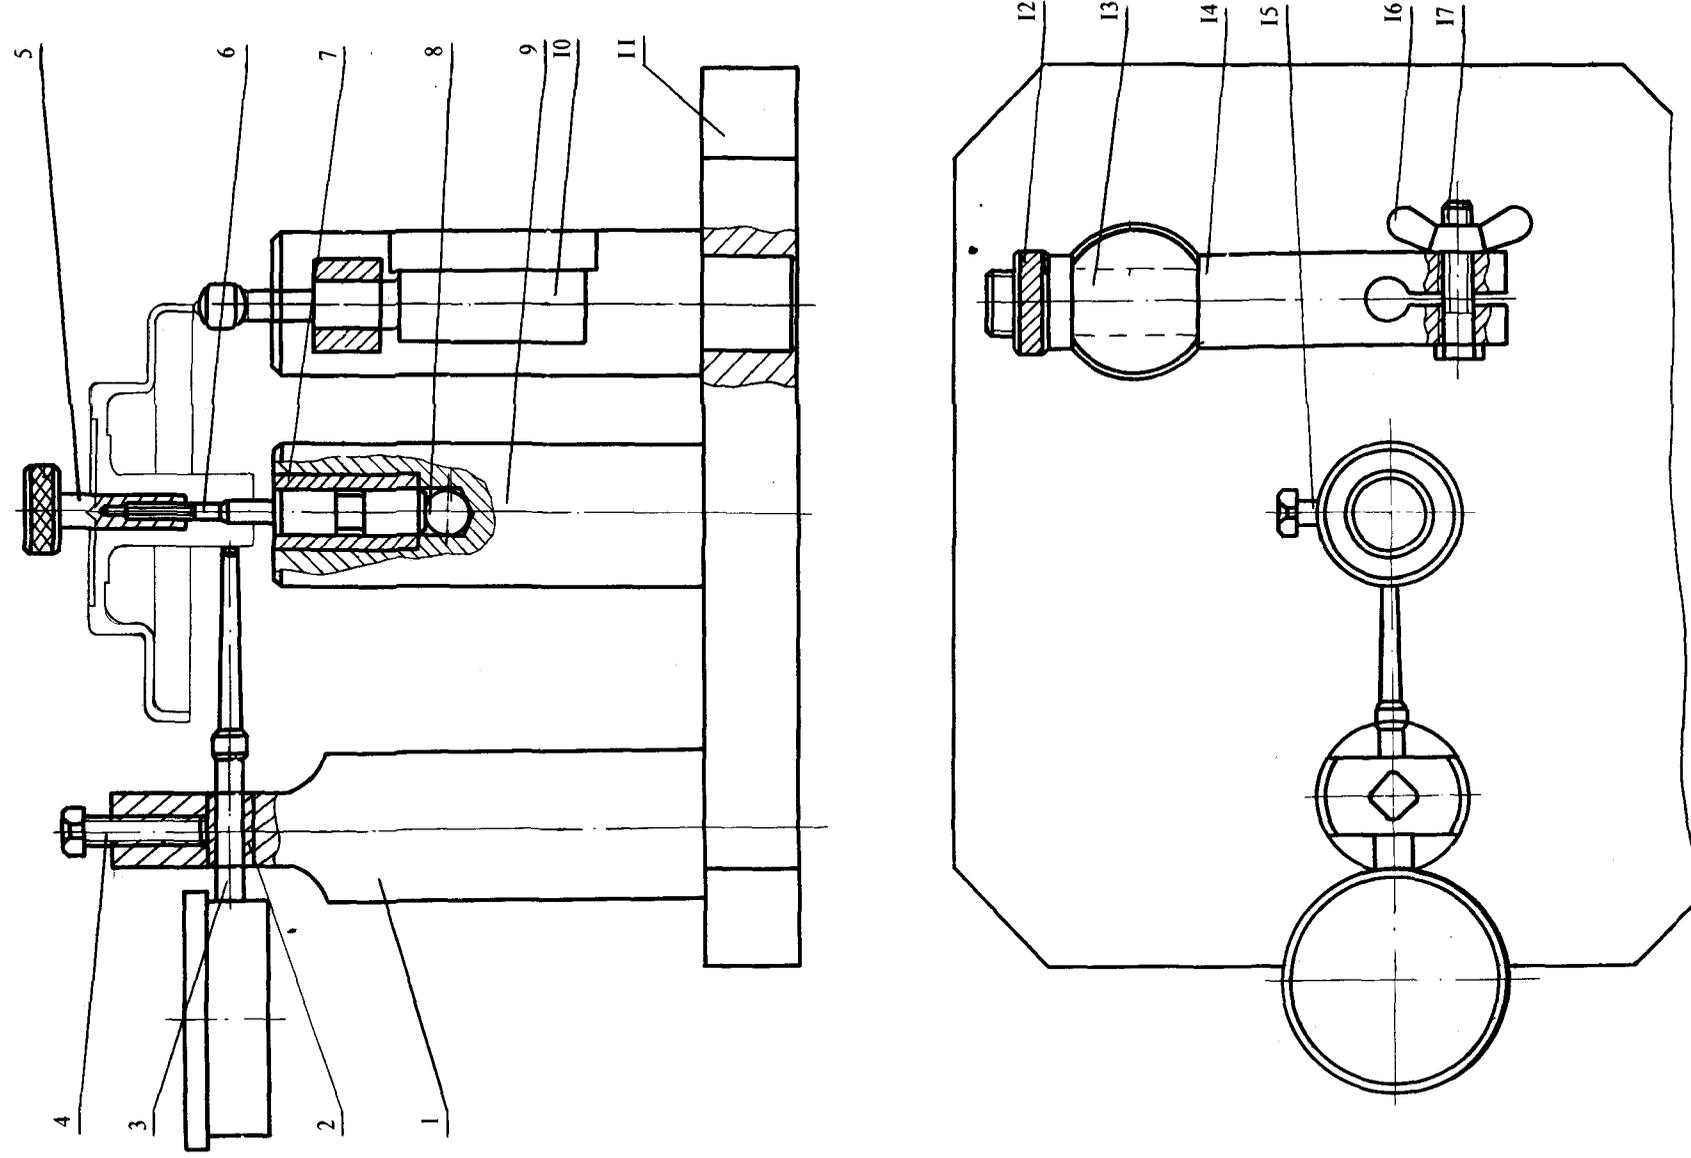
Контрольное приспособление для проверки биения ступицы и торца:
